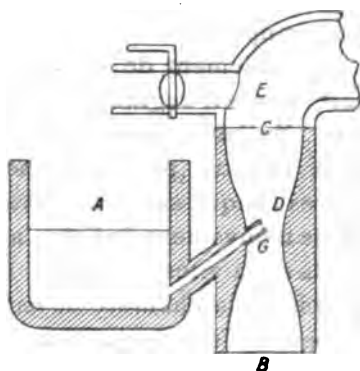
Carburateur avec prise d'air additionnel réglable.
